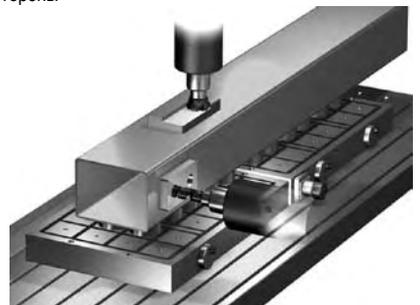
F - чистовая обработка и сверление трубчатых заготовок
